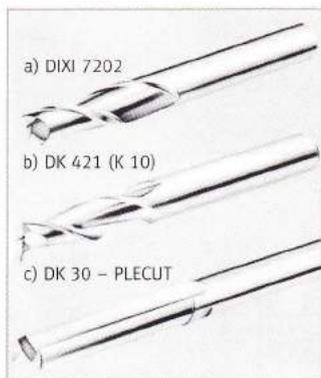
Оптимальные фрезы для прорезки пазов и обрезания кромки
